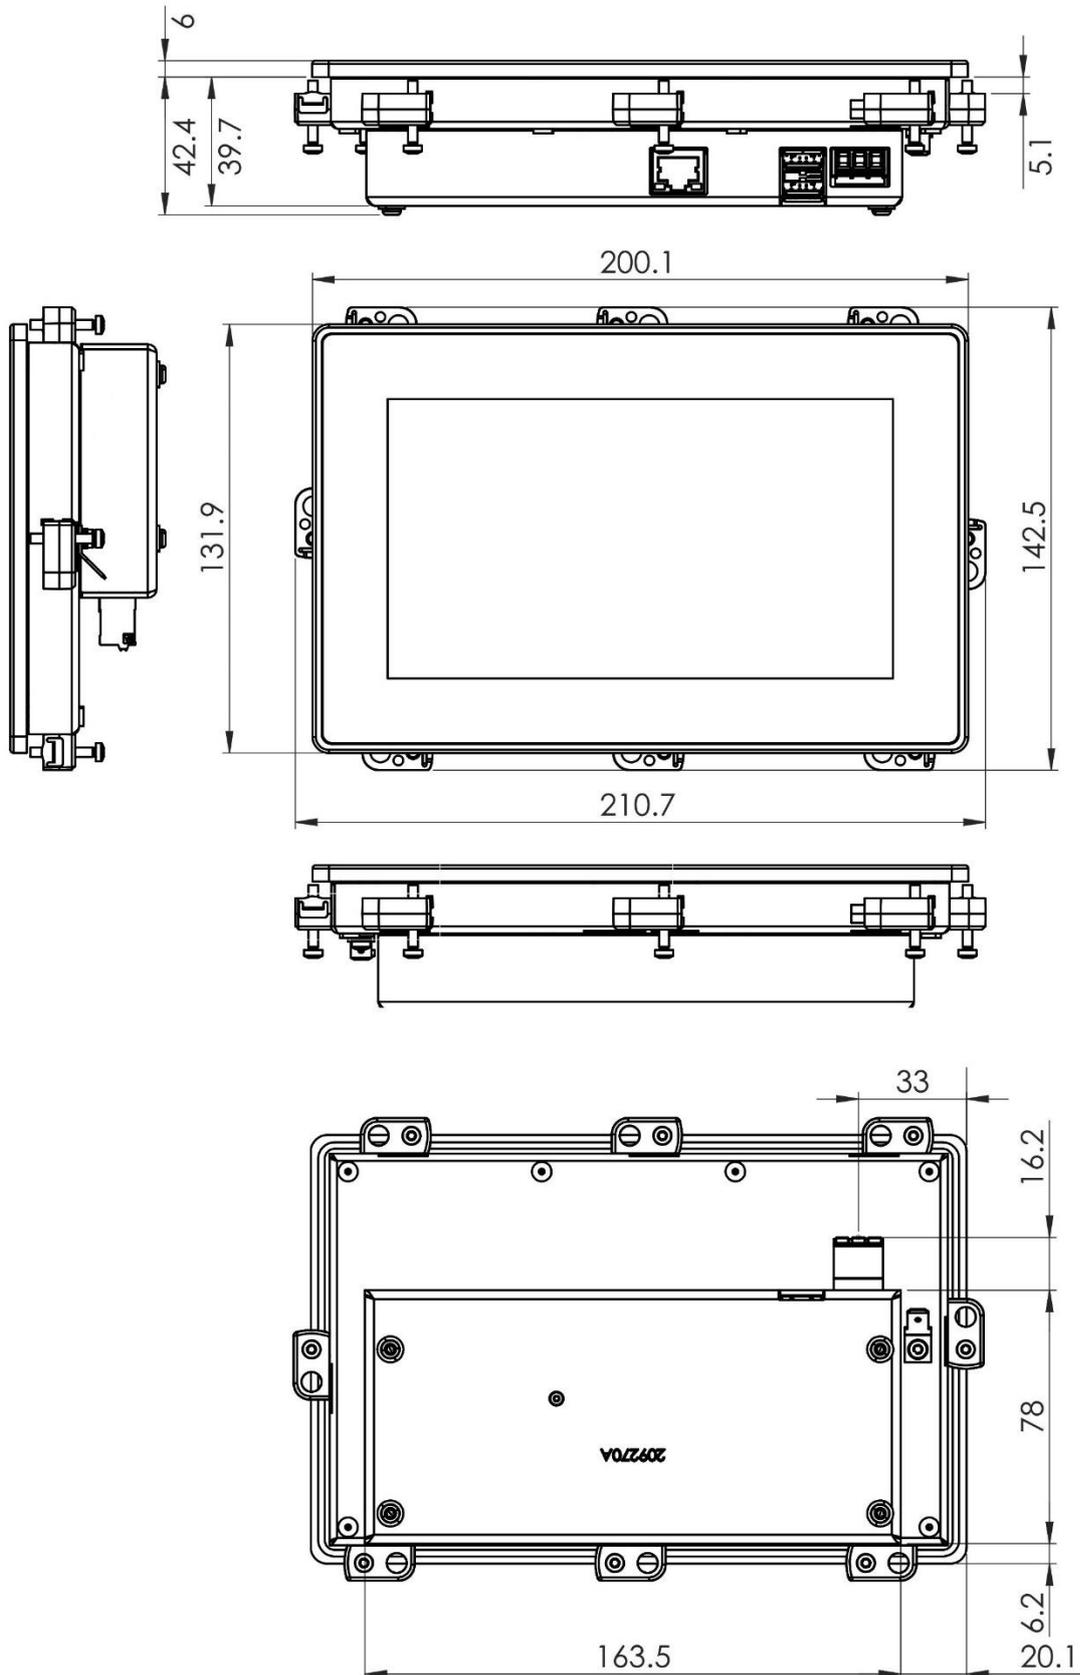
WP-70g 44-12x0 Montageausschnitt
